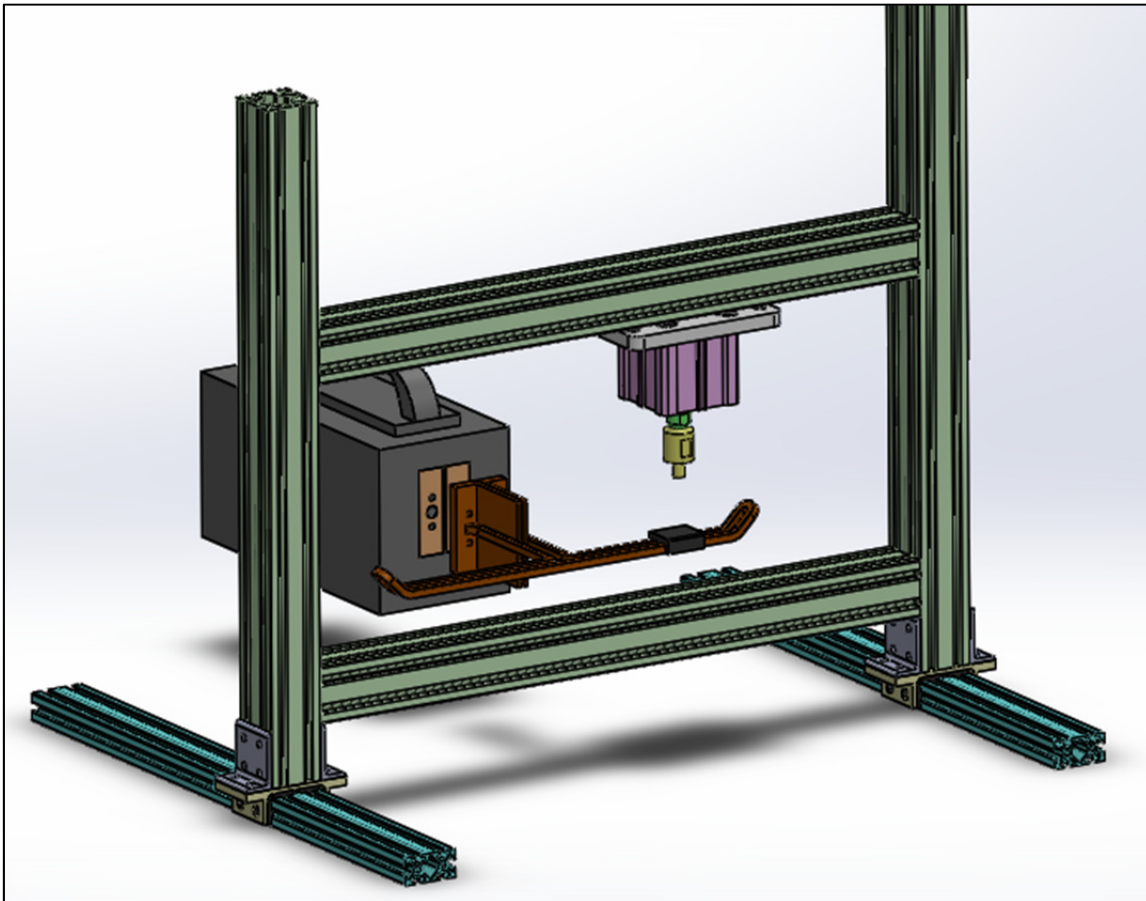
Montage de soudure sans sa table de support en céramique
